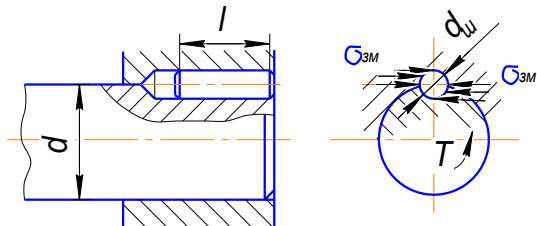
Схема з'єднання з циліндричною шпонкою
